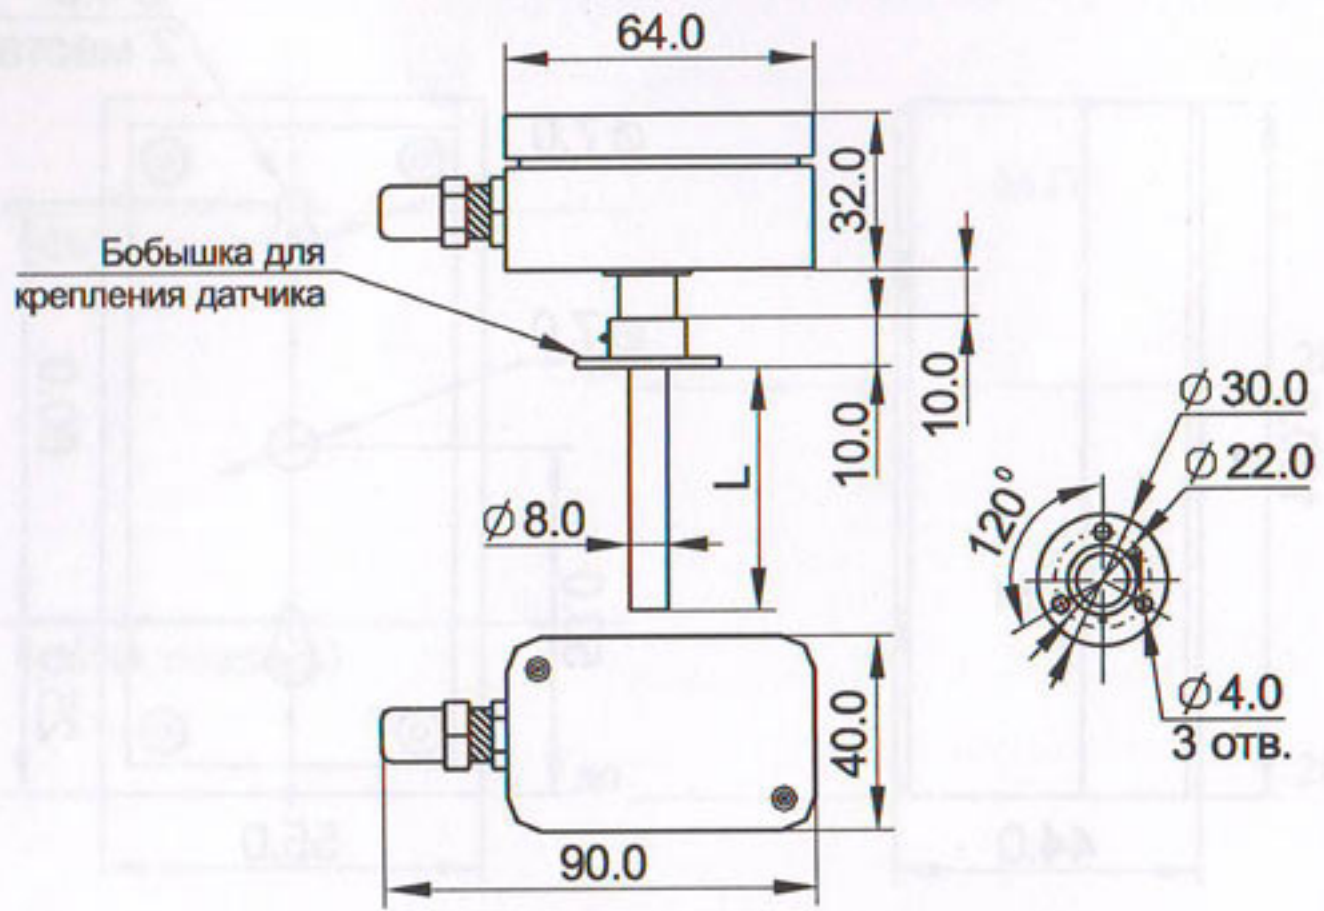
Конструктивные особенности и габаритно-присоединительные размеры датчика СТa-01
